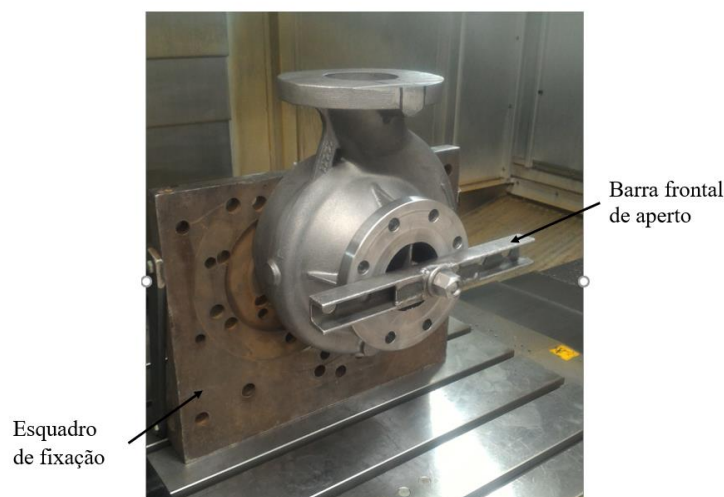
Componentes de fixação na 3ª fase de maquinagem do corpo da bomba.
